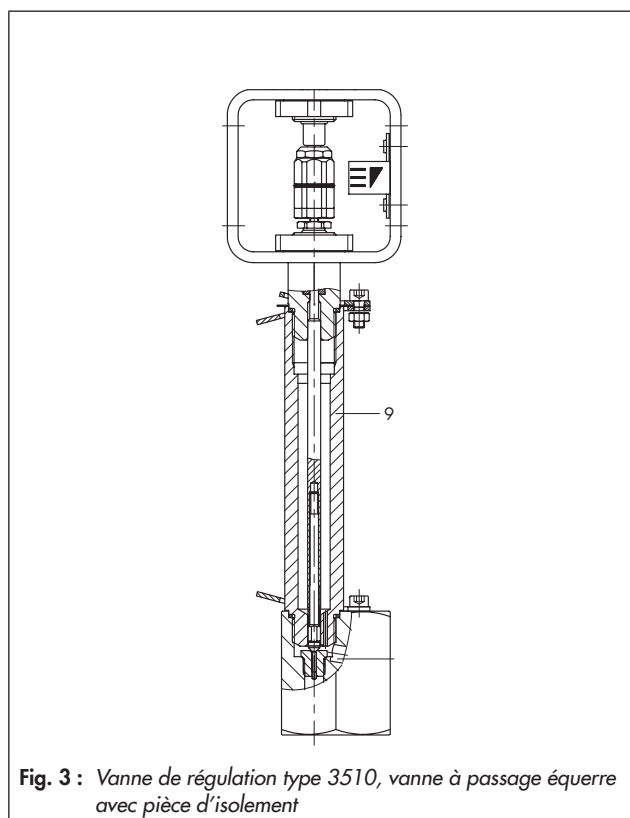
Vanne de régulation type 3510, vanne à passage équerre avec pièce d'isolement
